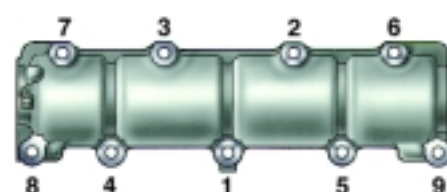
Порядок затяжки гаек крепления корпуса подшипников распределительного вала двигателя мод. 2106–70
